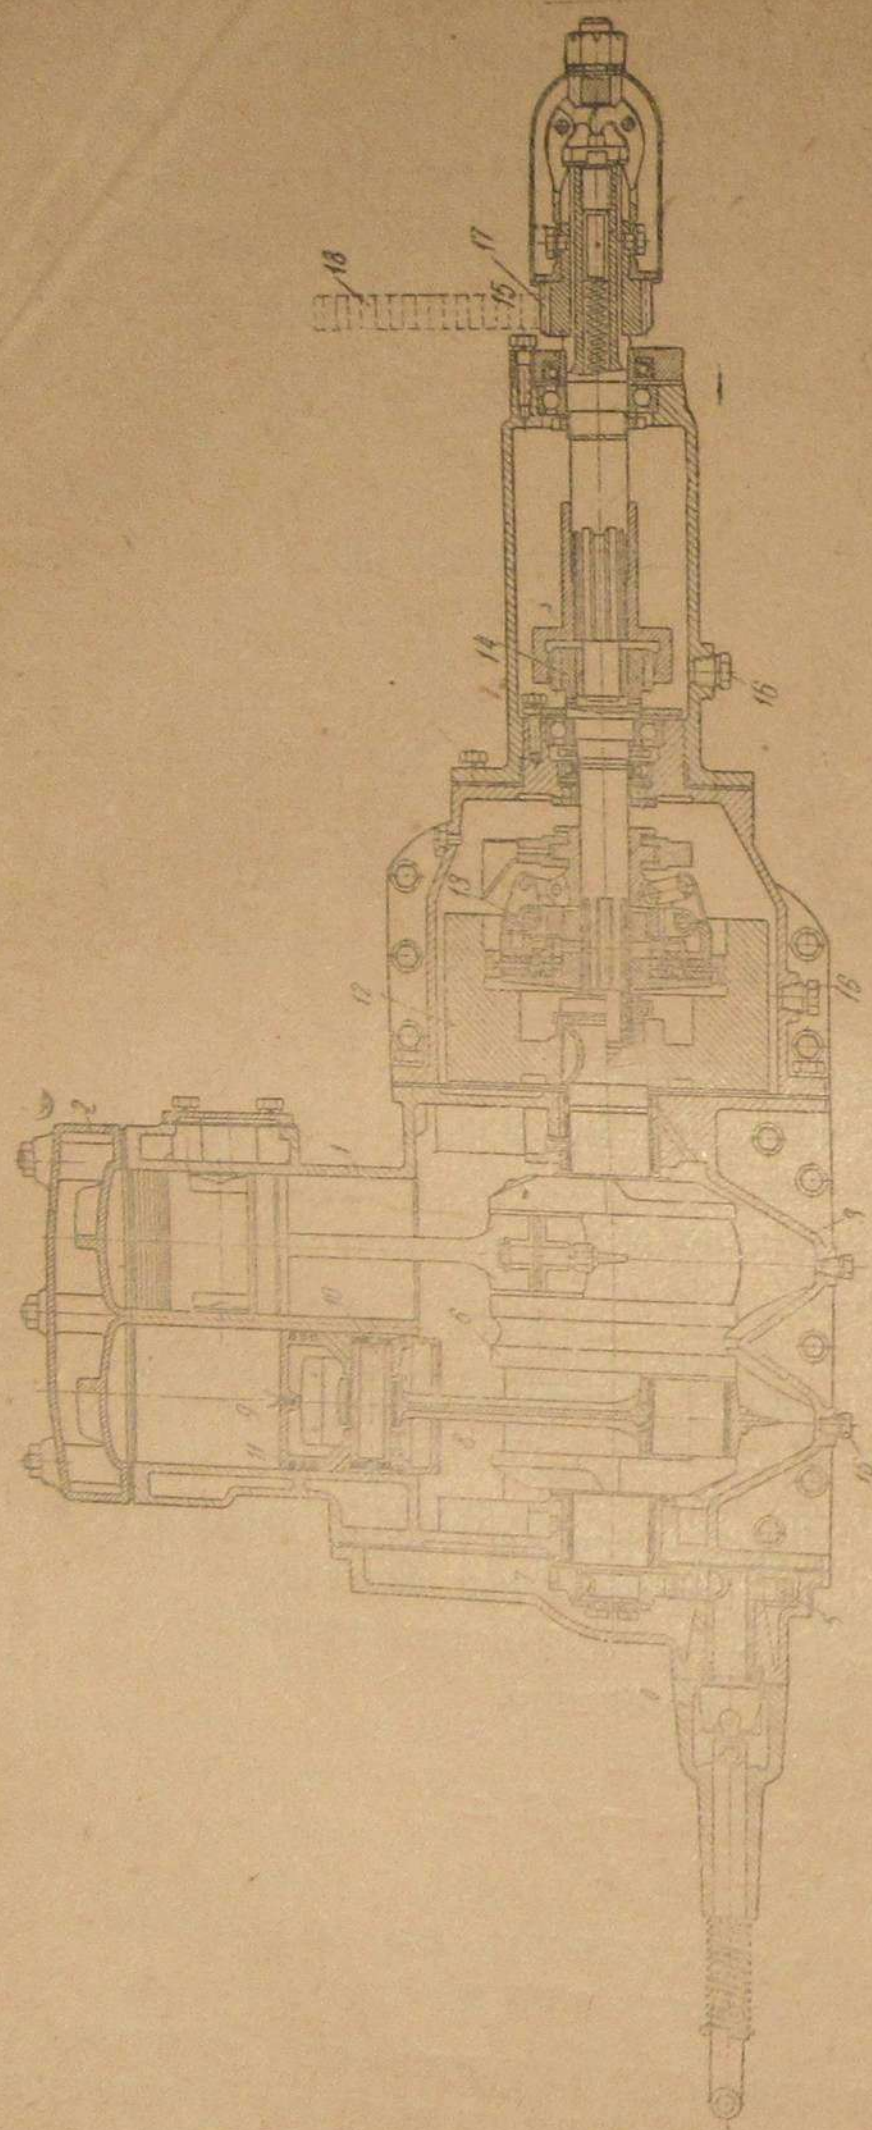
Продольный разрез пускового двигателя В-20: 1 — блок цилиндров, 2 — головка блока цилиндров, 3 — картер, 4 — пусковое приспособление, пусковая рукоятка, 5 — шестерня пускового приспособления, 6 — коленчатый вал, 7 — шестерня коленчатого вала, 8 — шатун, 9 — поршень, 10 — поршневой палец, 11 — поршневое кольцо, 12 — маховик, 13 — механизм включения, 14 — соединительная муфта, 15 — механизм включения, 16 — спусковые пробки, 17 — шестеренка мотора, 18 — маховик главного двигателя
